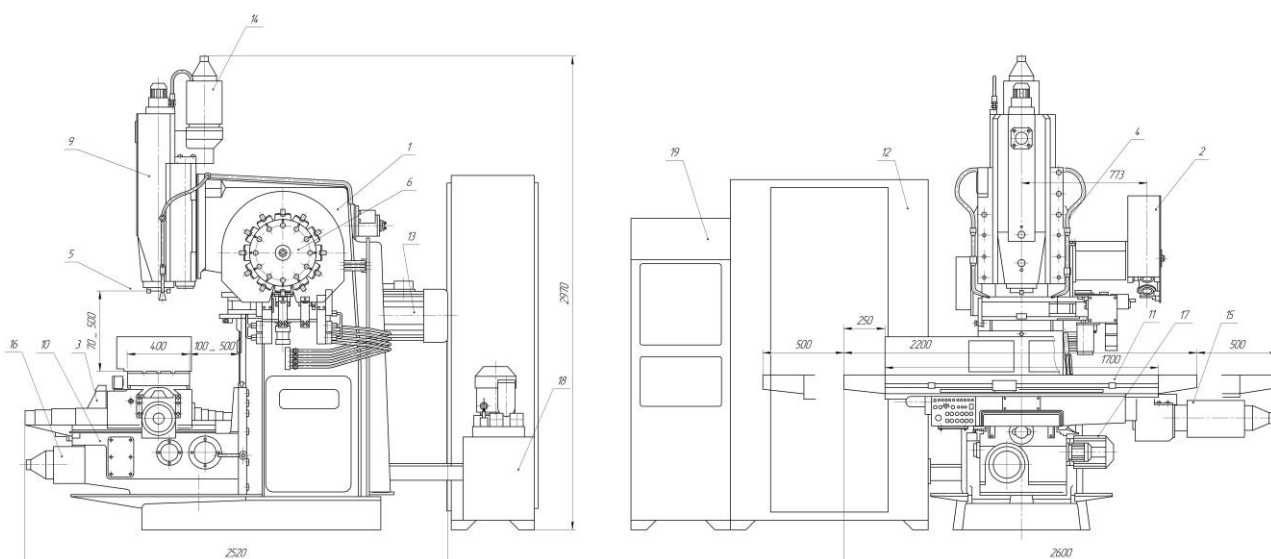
Загальний вигляд верстата вертикально фрезерувального моделі 6Р13Ф3
